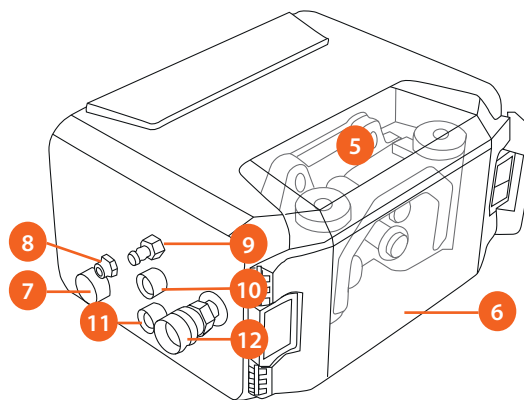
Механизм подачи проволоки – вид сзади
